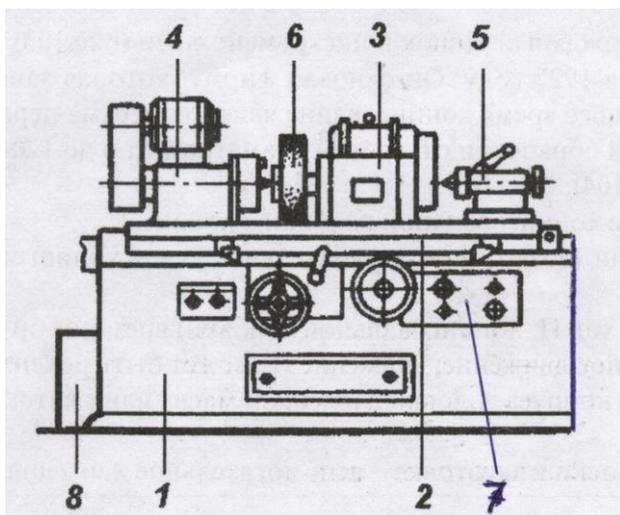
Схема внешнего вида круглошлифовального станка: 1 – станина; 2 – стол; 3 – шлифовальная бабка; 4 – передняя бабка; 5 – задняя бабка; 6 – шлифовальный круг; 7 – панель управления; 8 – гидросистема для смазывающе-охлаждающей жидкости
